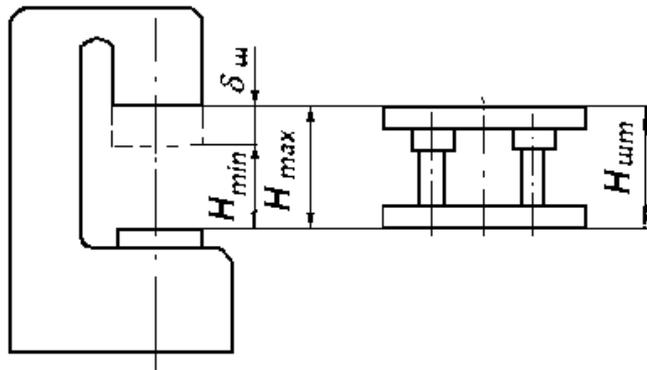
Схема для определения меж штампового пространства прессы и закрытой высоты штампа
